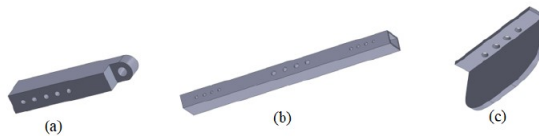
Componentes de suporte. (a) barra ajustável com uma junta de 1 DOF; (b) Conector das pernas; (c) Placa rígida com furos de fixação.
